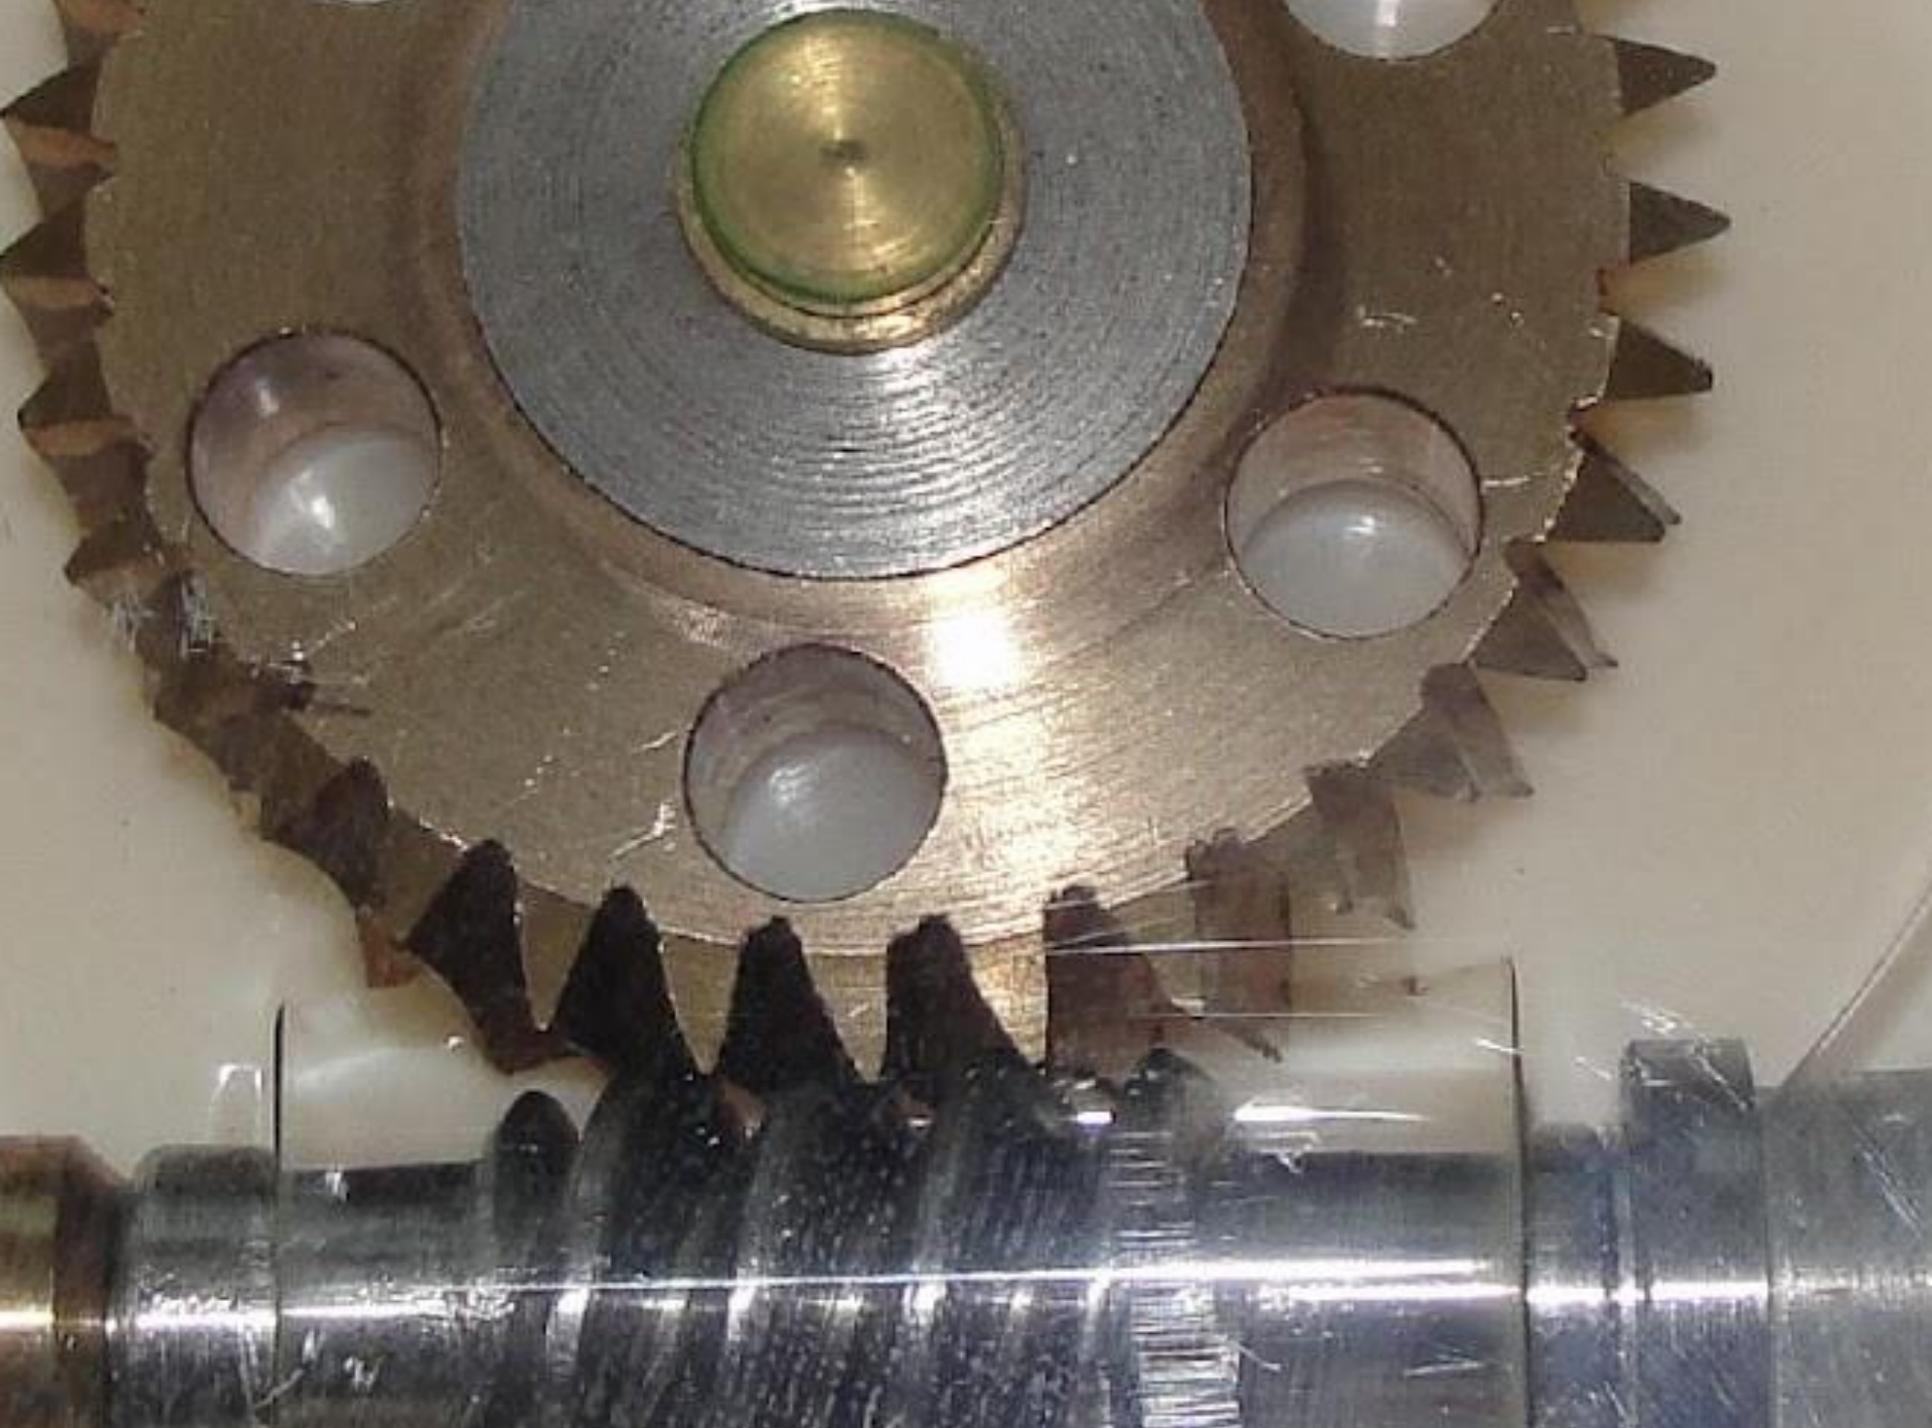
Червячный редуктор с нижним расположением червяка
